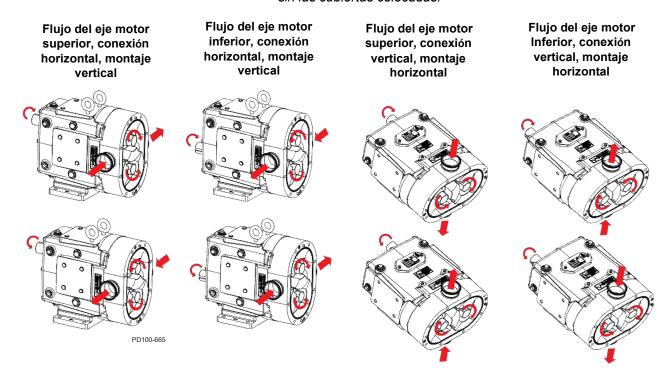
Rotación de la bomba (se muestra el extremo del líquido)
